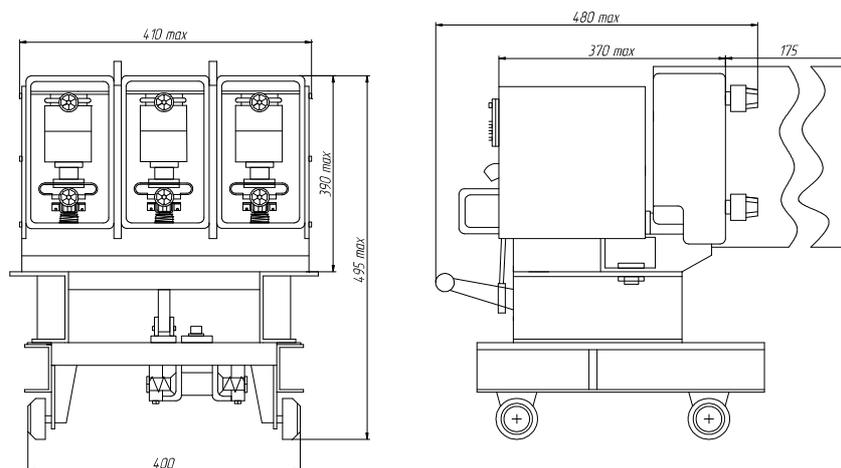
Габаритные и установочно-присоединительные размеры выключателя (выкатное исполнение)
